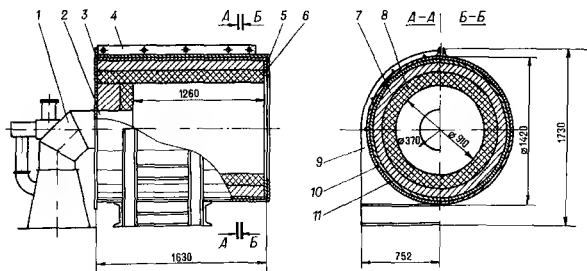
Выходная топка ВТ-2,8 конструкции ЛИСИ для барабанных сушил.
